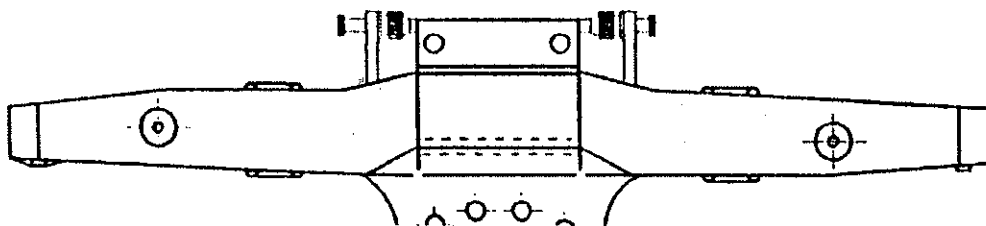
Контроль сварного соединения кронштейна скользуна с балкой
